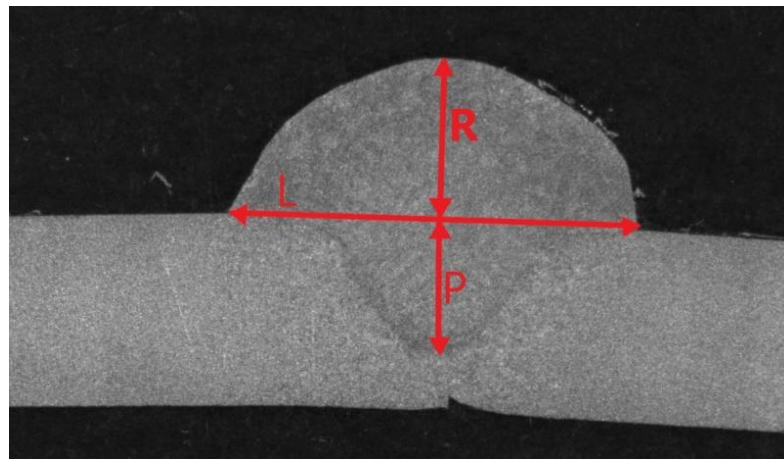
Medições realizadas nos cordões de solda (R – reforço, L – largura e P – penetração).
